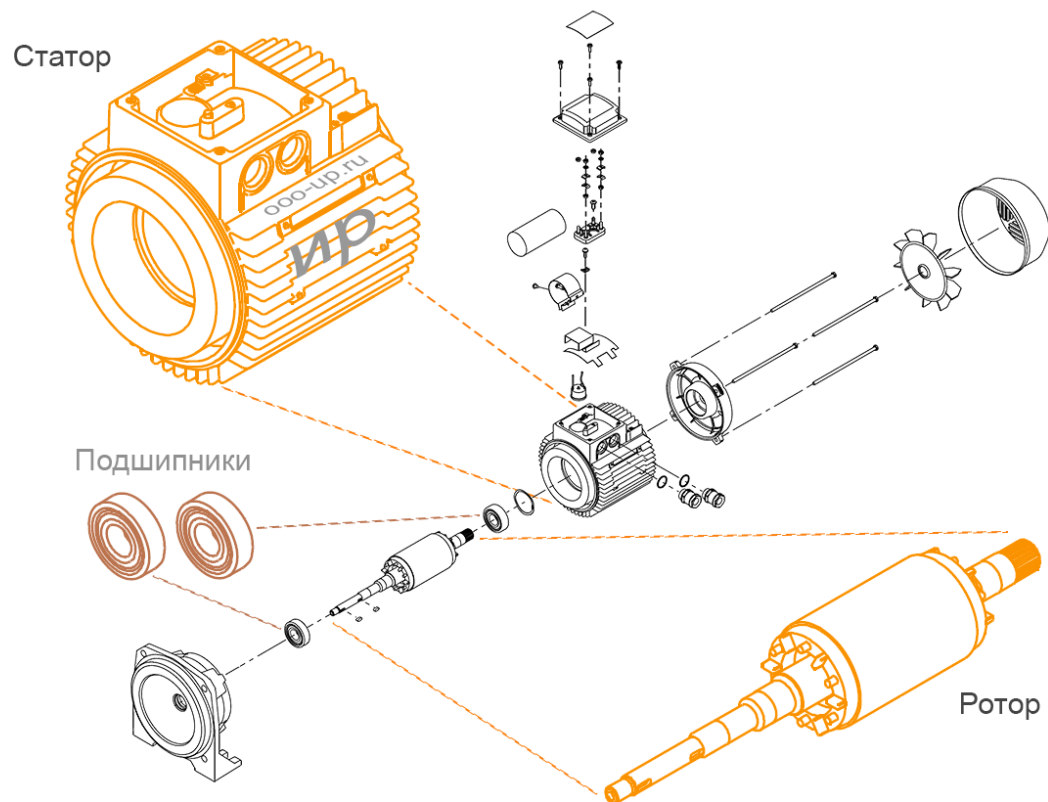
Стандартная конструкция вращающегося электродвигателя
